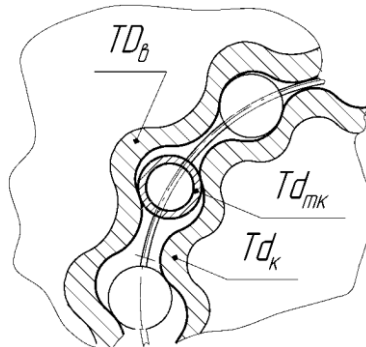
Схема расположения допусков в зацеплении передачи с ПТК и свободной обоймой.
